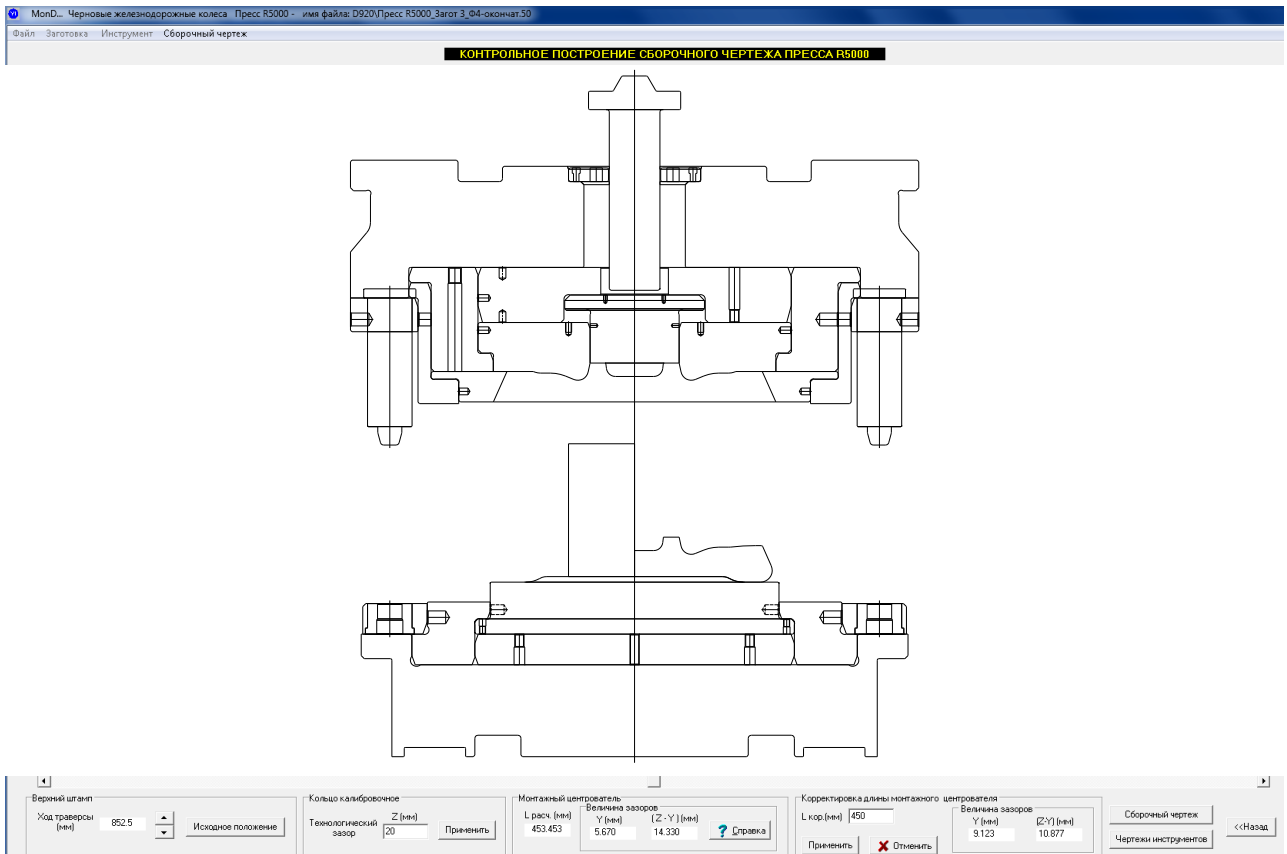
Проектирование сборочного чертежа инструмента деформации заготовочного пресса
